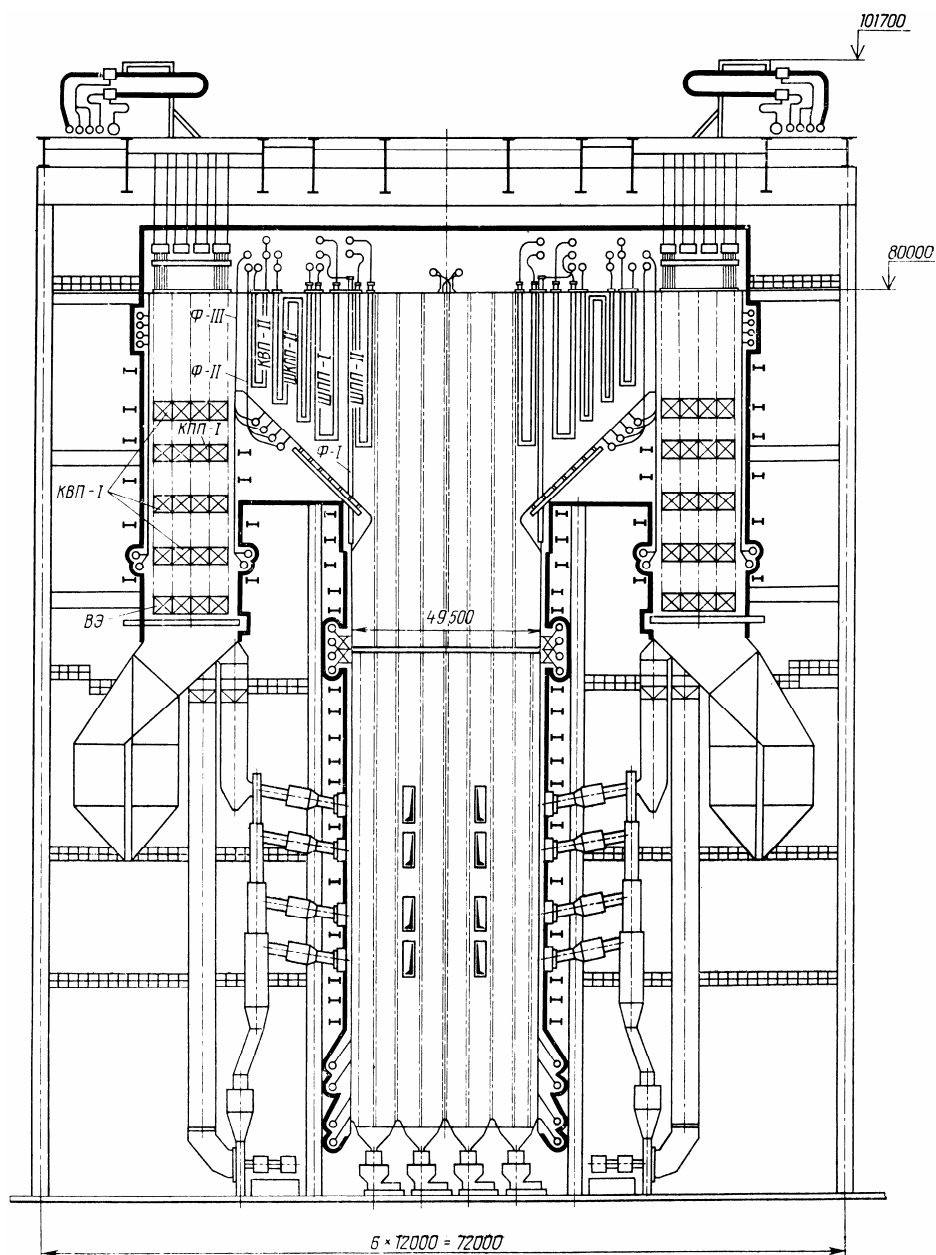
Поперечный разрез котла Пп-1650-25-545/542 БТ (П-75)
